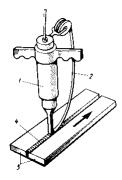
Схема сварки с дополнительной присадкой: 1 — преобразователь с волноводом-инструментом; 2 — присадочный материал; 3 — свариваемые детали; 4 — шов.
